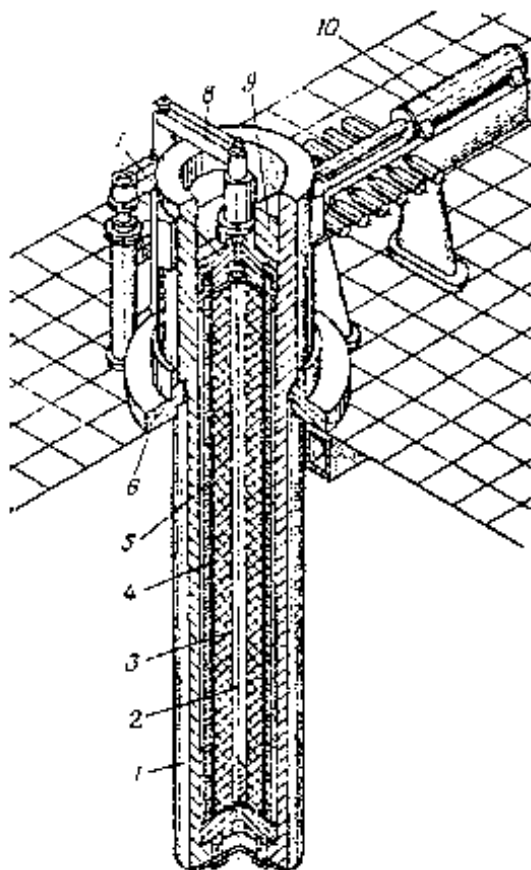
Схема гидростатической установки для двухстадийного формования изделий [12]:
